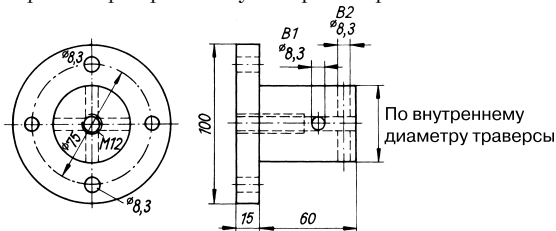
Рабочий эскиз втулки с фланцем из легкого сплава
